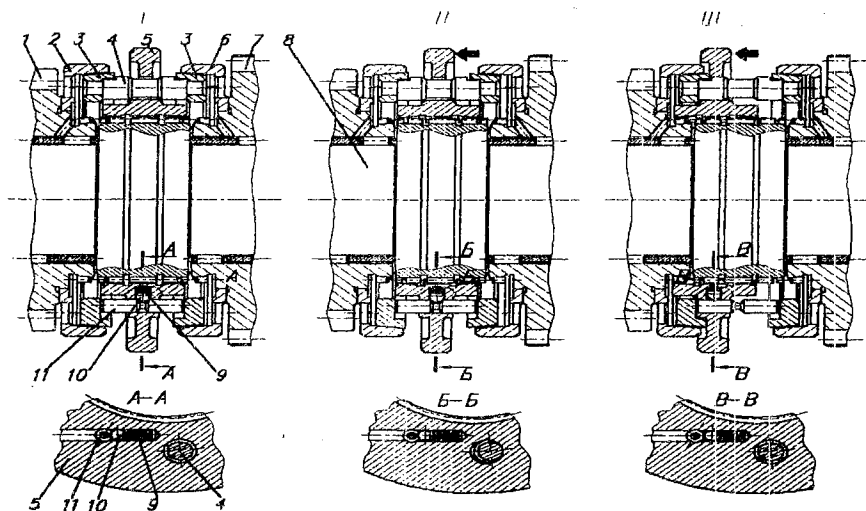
Синхронизатор второй и третьей передачи коробки ЯМЗ-202 и его работа: 1 – шестерня третьей передачи; 2 – фрикционный конус шестерни третьей передачи; 3 – фрикционные конусные кольца синхронизатора; 4 – блокирующий палец; 5 – каретка синхронизатора; 6 – фрикционный конус шестерни второй передачи; 7 – шестерня второй передачи; 8 – вторичный вал базовой коробки передач; 9 – пружина фиксатора; 10 – шарик фиксатора; 11 – палец фиксатора; I – нейтральное положение муфты синхронизатора; II – начало включения синхронизатора; III – передача включена
